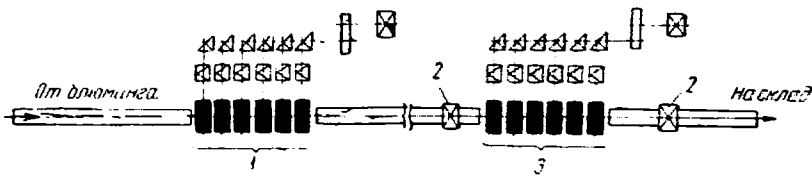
Схема расположения непрерывного заготовочного стана 630/450 с групповым приводом:
